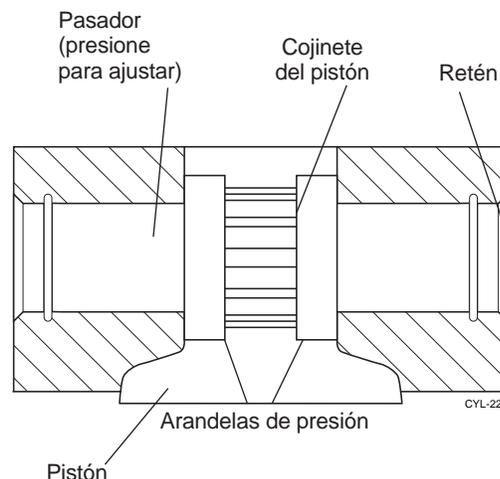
Conjunto de pasador del pistón, cojinete y arandelas de presión
